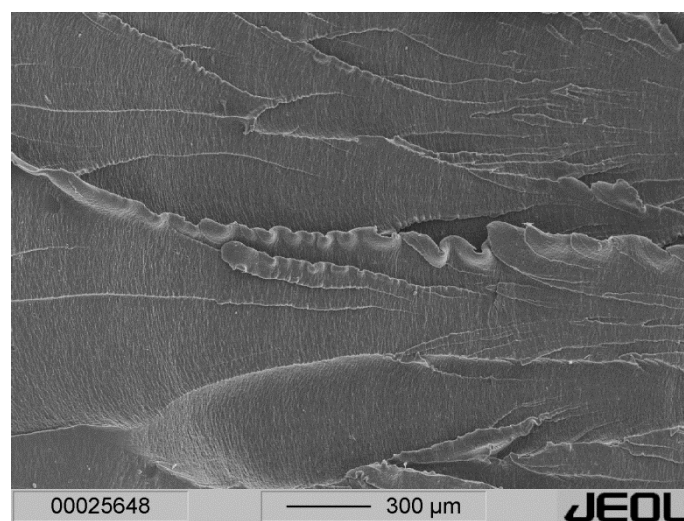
Bruchflächenmerkmal Bruchparabeln/U- oder V-förmige Rampen in multipler Ausführung bei duktilem Werkstoffverhalten [2], PP mit hohem Molekulargewicht
